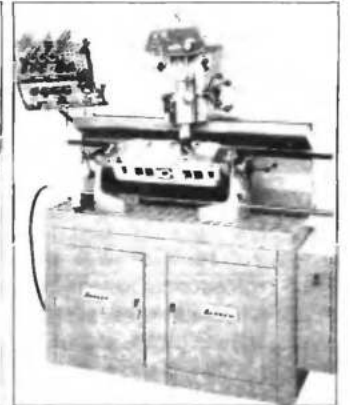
Станок для комплексного ремонта головок блока цилиндров
